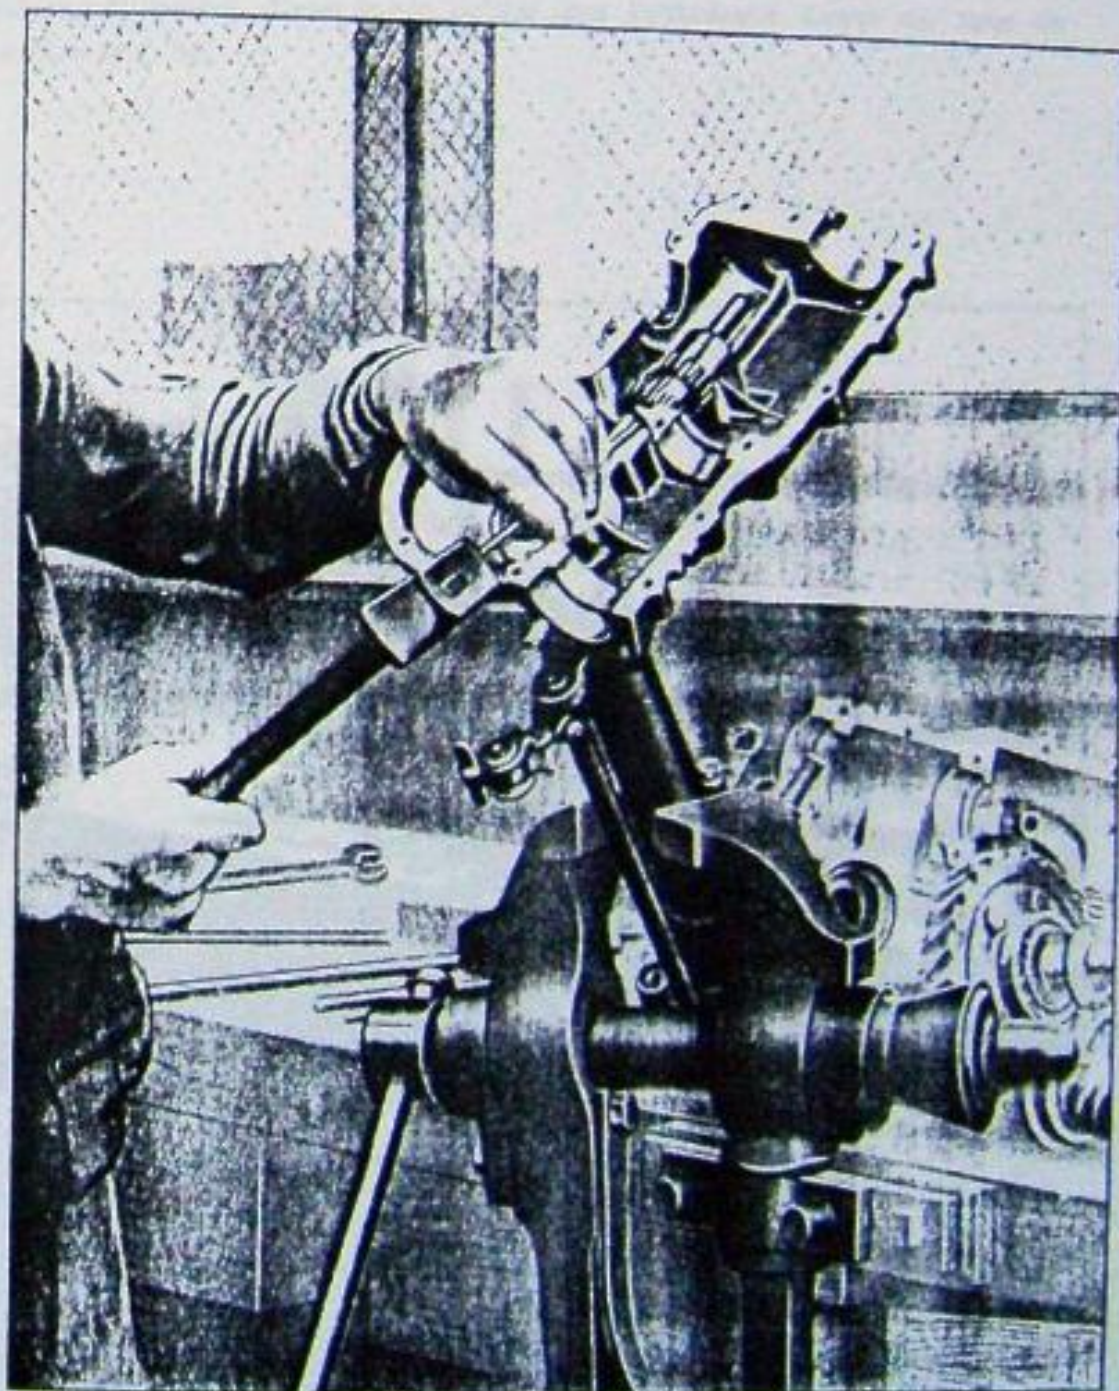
Enlèvement de l'arbre de marche arrière.
